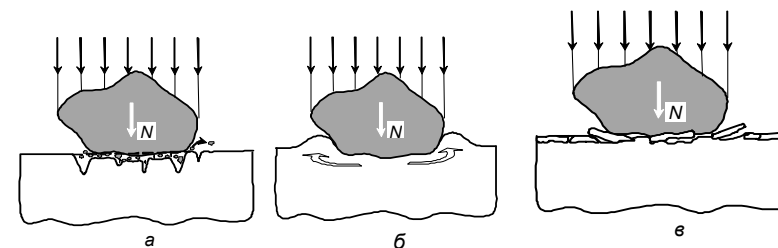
Механизмы гидроабразивного изнашивания деталей
